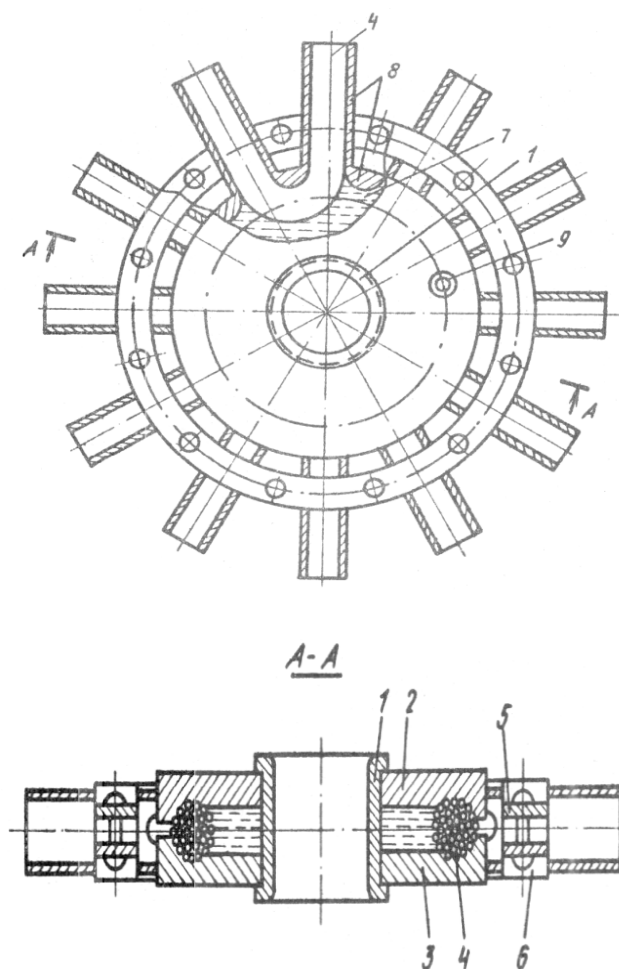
Схема радиальной щетки цилиндрической формы с U-образными пучками ворсовых элементов и кольцевой камерой для пластичного смазочного материала
